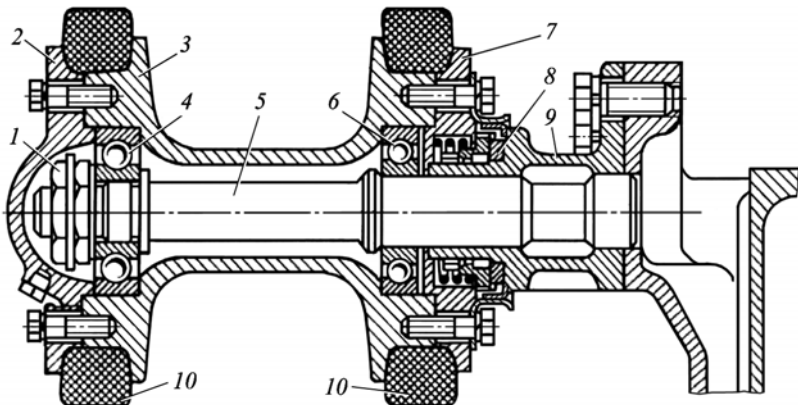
Підтримувальний ролик трактора Т-150:
